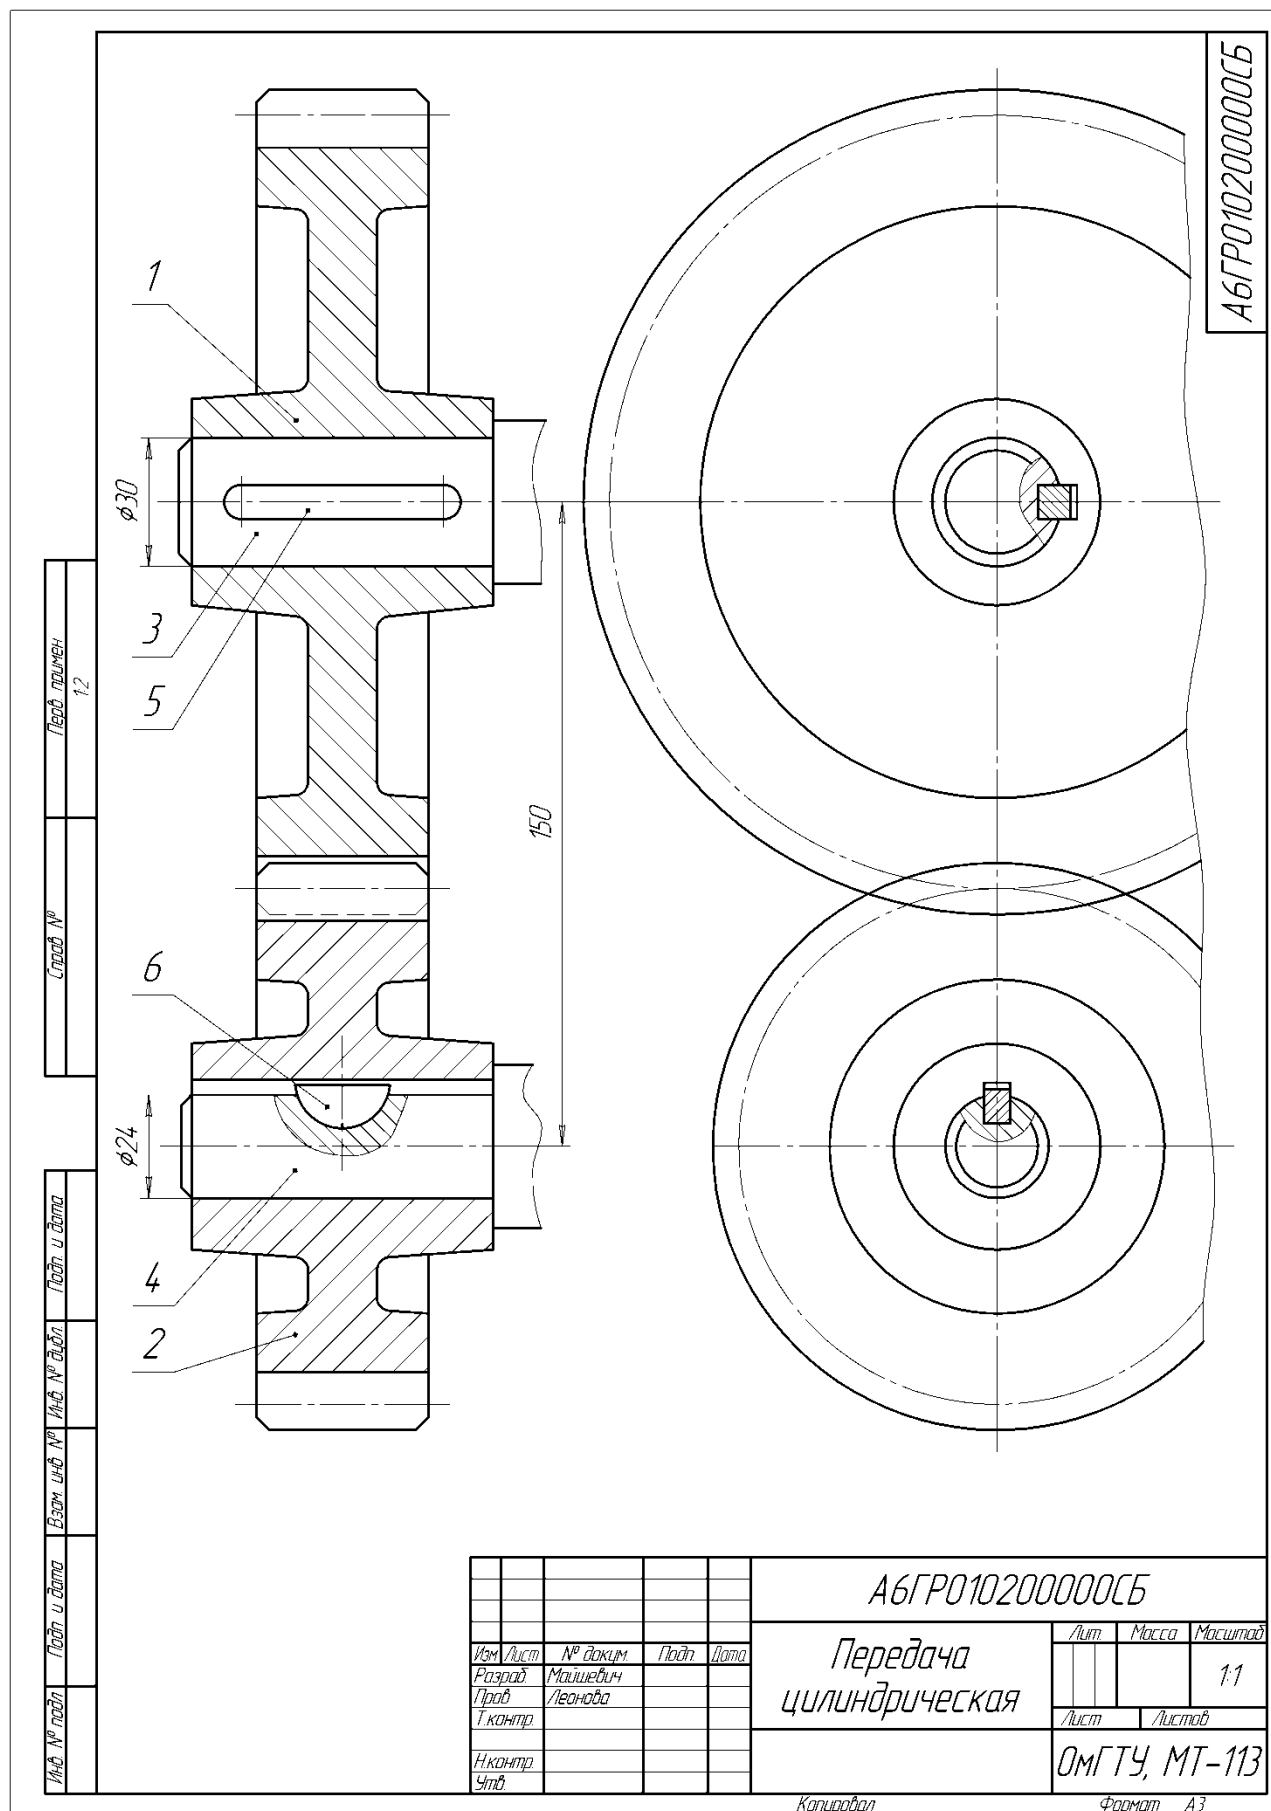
Сборочный чертеж зубчатой передачи со шпоночным соединением валов и колес
